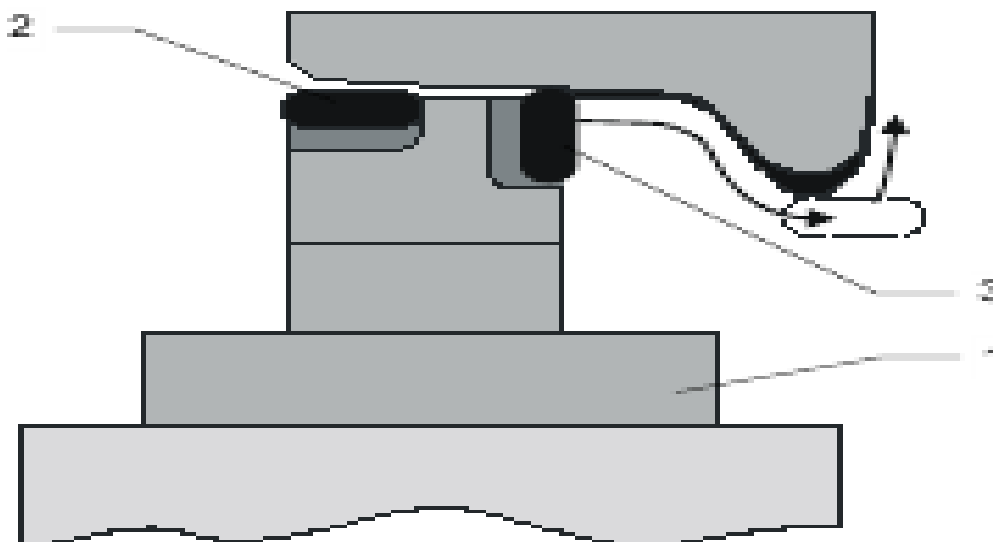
Обробка профілю кочення (1 – різцетримач; 2 – пластина для обробки внутрішньої сторони гребеня; 3 – пластина для обробки зони кочення та робочої сторони гребеня)
